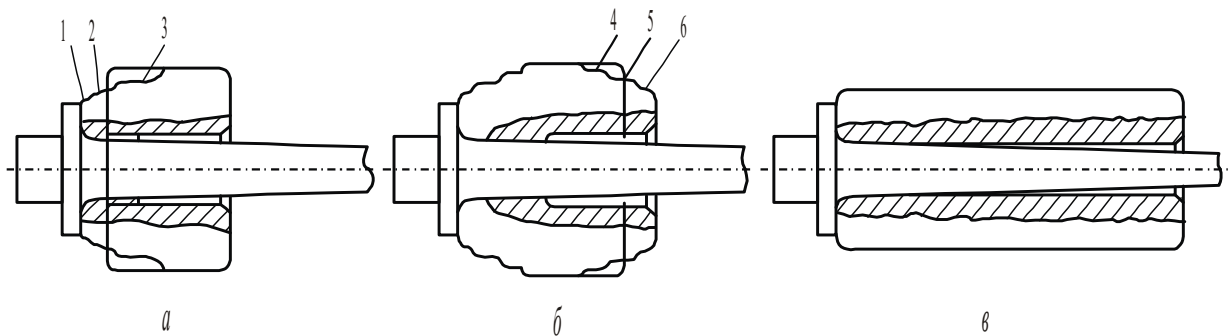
Етапи протяжки прошитої заготовки на конічній оправці
